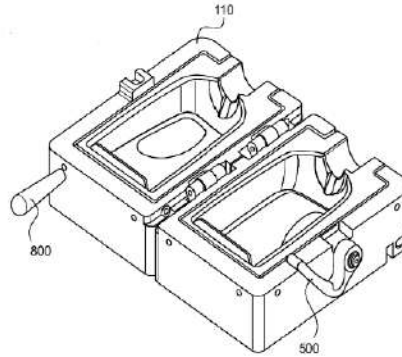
Diseño de molde para embalaje biodegradable, patente US-20170225381A1
